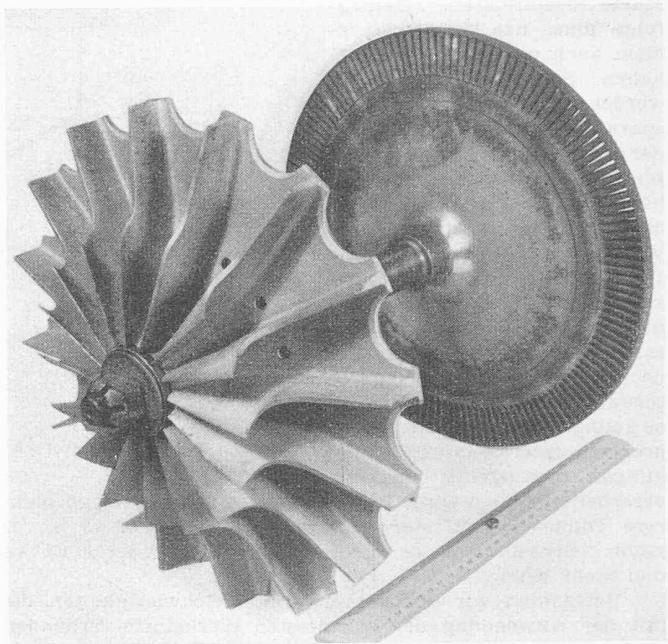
Abgasturbine mit Gebläse für ein Flugzeug
